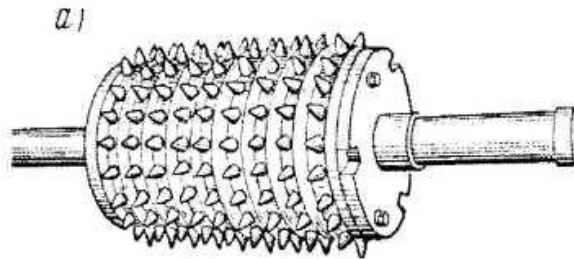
Конструкція зубчастого валка з набірних кілець
